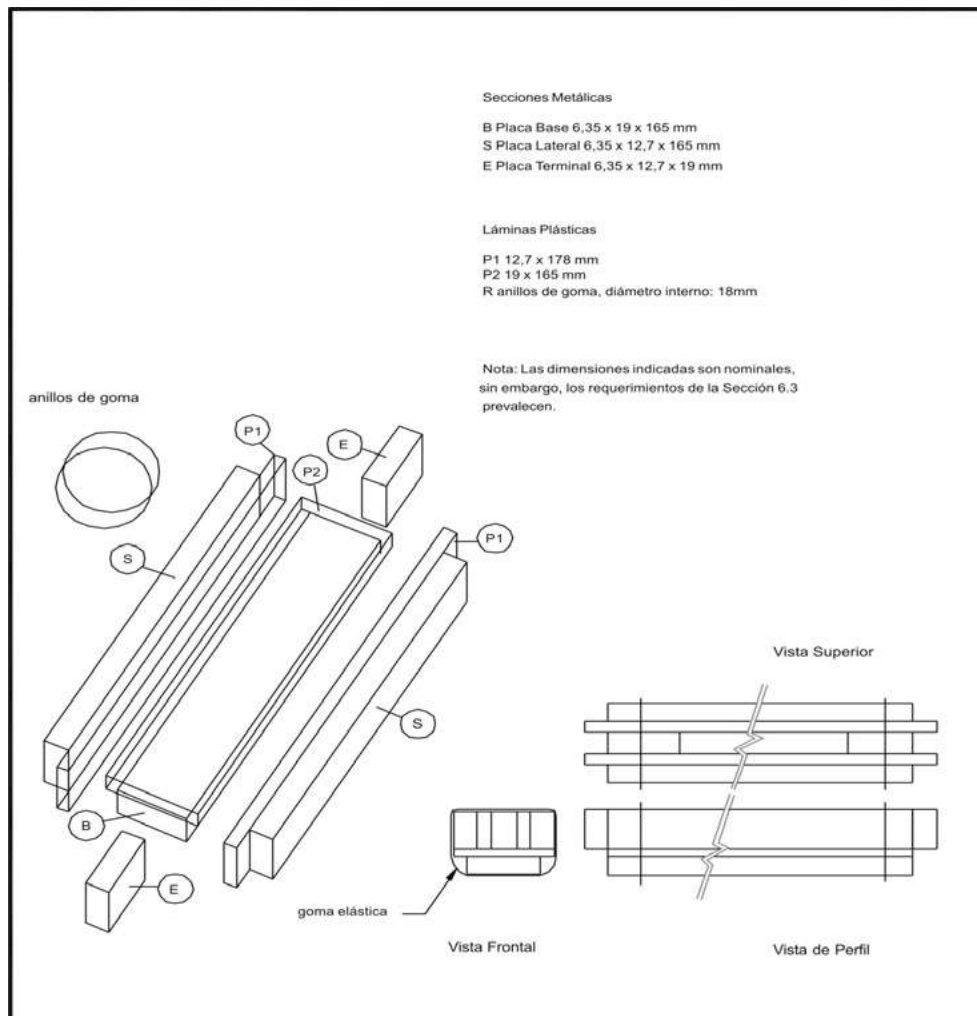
26. DIMENSIONES Y ESPECIFICACIÓN PARA LOS MOLDES DE ALUMINIO
